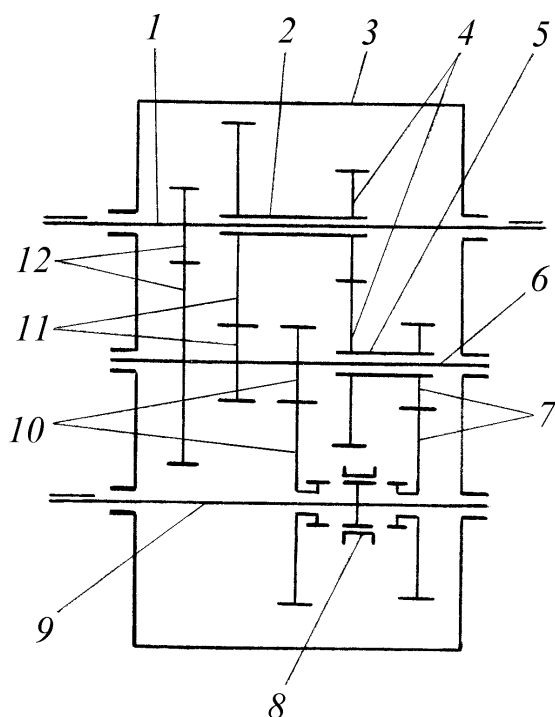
Схема двухдиапазонного ходоуменьшителя с неподвижными осями валов
